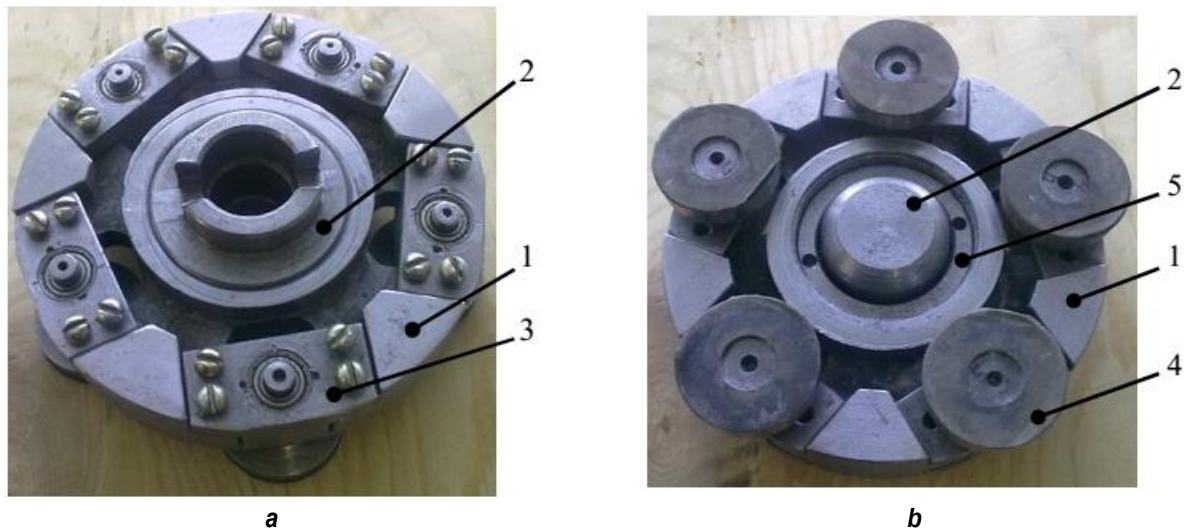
Пятидисковая шлифовальная головка: а – вид сверху; б – вид снизу; 1 – планшайба; 2 – съемная ступица; 3 – вставка; 4 – рабочий диск с абразивной шкуркой; 5 – контрольная гайка
